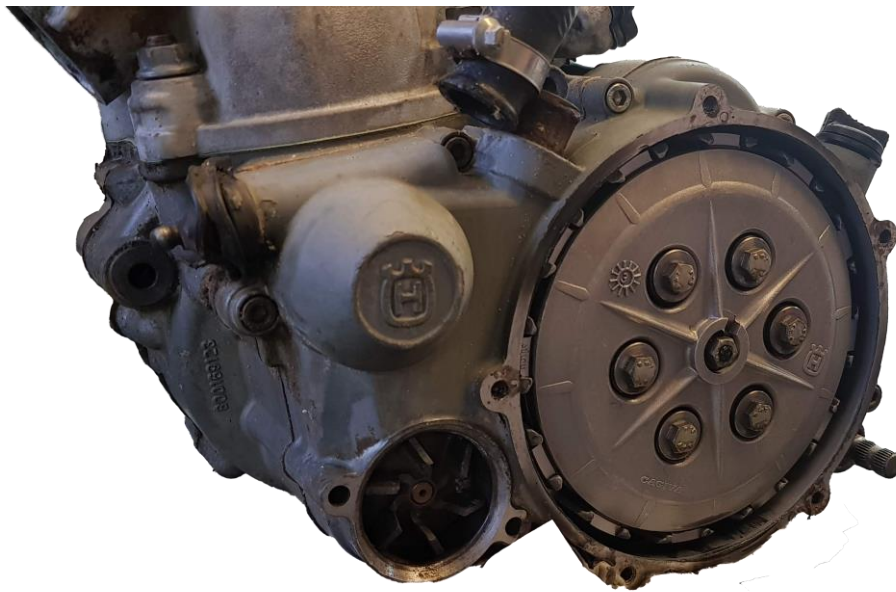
Conjunto del embrague a la vista tras retirar la tapa.
